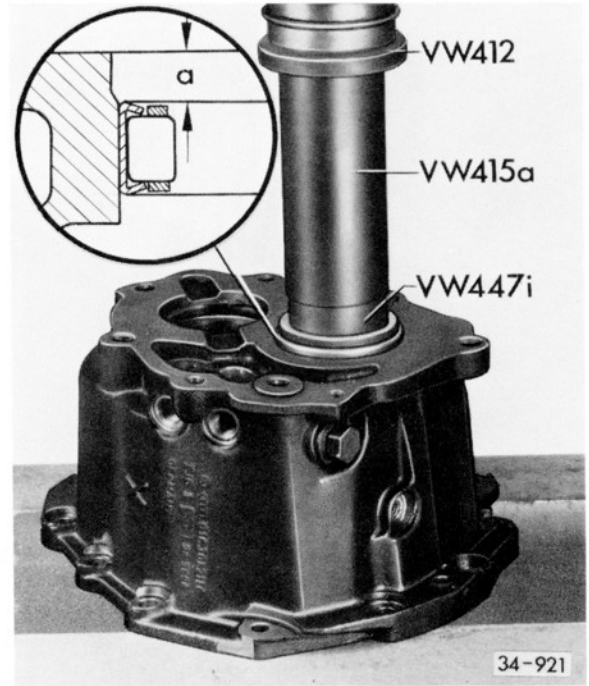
Außenring/Zylinderrollenlager in Lagerschild einpressen
